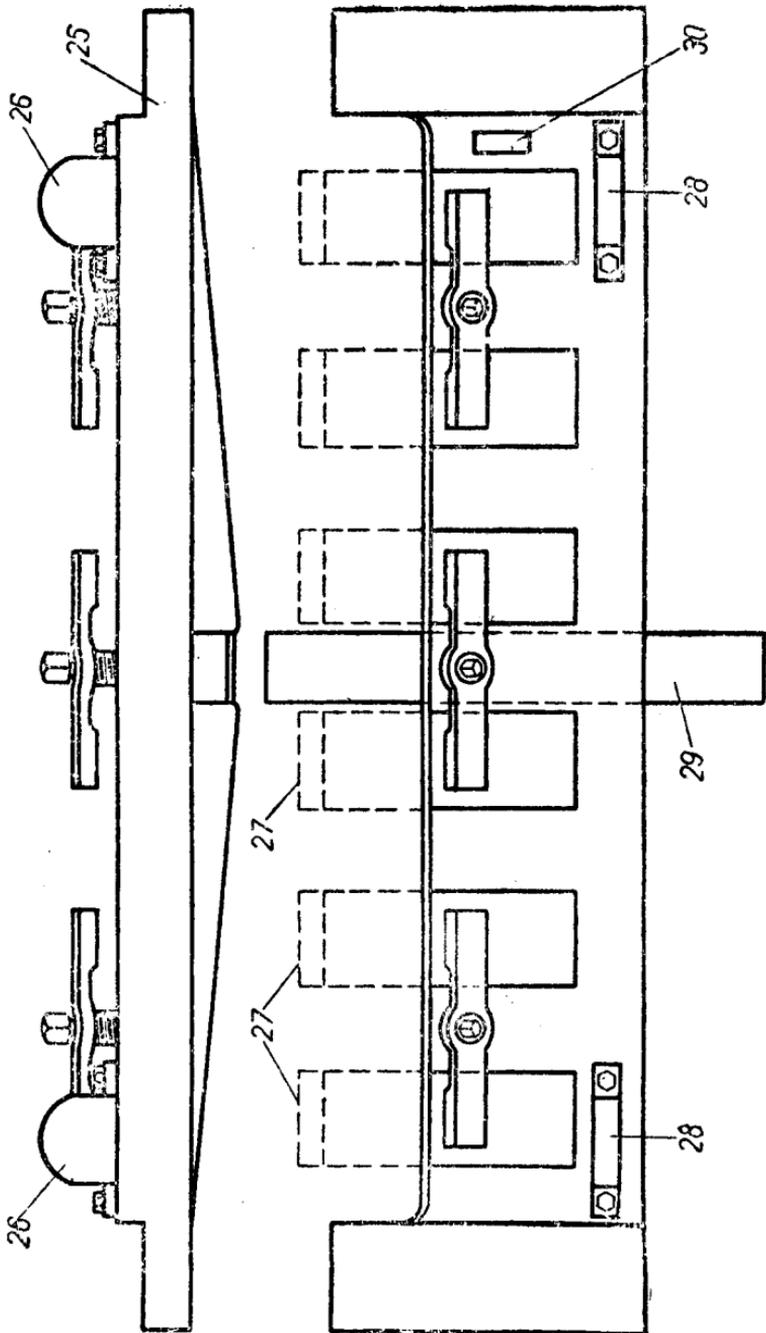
Проект станка т. Пурецкого. Приспособление для зажима болванок при операциях 2-й и 3-й: 26—копир для роликов; 27—зажатые болванки; 28—копир; 29—зажатая рейка; 30—за этот зуб захватывает крючок зубчатой рейки, изображенный на рисунках 60, 61 и 62 и служащий для поперечного перемещения этого приспособления.
